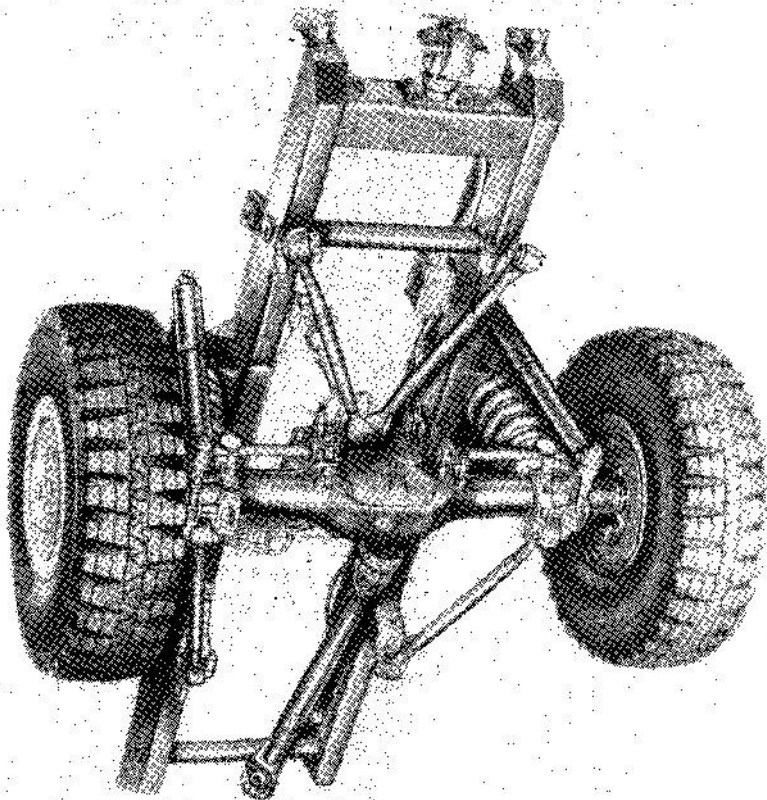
Вид снизу на заднюю подвеску полноприводного внедорожного грузового автомобиля фирмы МАН грузоподъемностью 6 т. Передние продольные штанги имеют длину 1025 мм, а задний треугольный рычаг с очень широкой опорной базой — длину 762 мм. Такие размеры вместе с высокими пружинами прогрессивного действия допускают угол перекоса между осью и рамой $15^{\circ}30'$. Буфера сжатия установлены внутри пружин, а буфера, ограничивающие ход отбоя, — внутри амортизаторов, расположенных благоприятным образом рядом с пружинами
